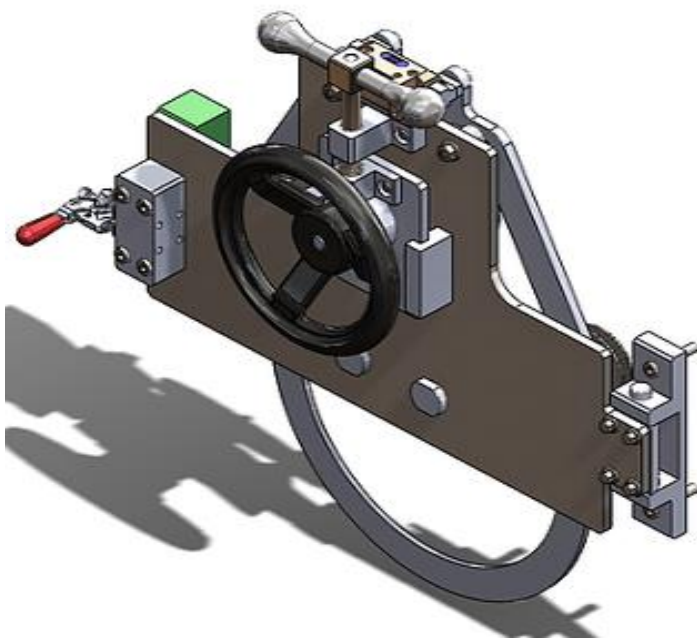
Sistema de fijación y accionamiento para el movimiento de rotación, en la soldadura de brida.
